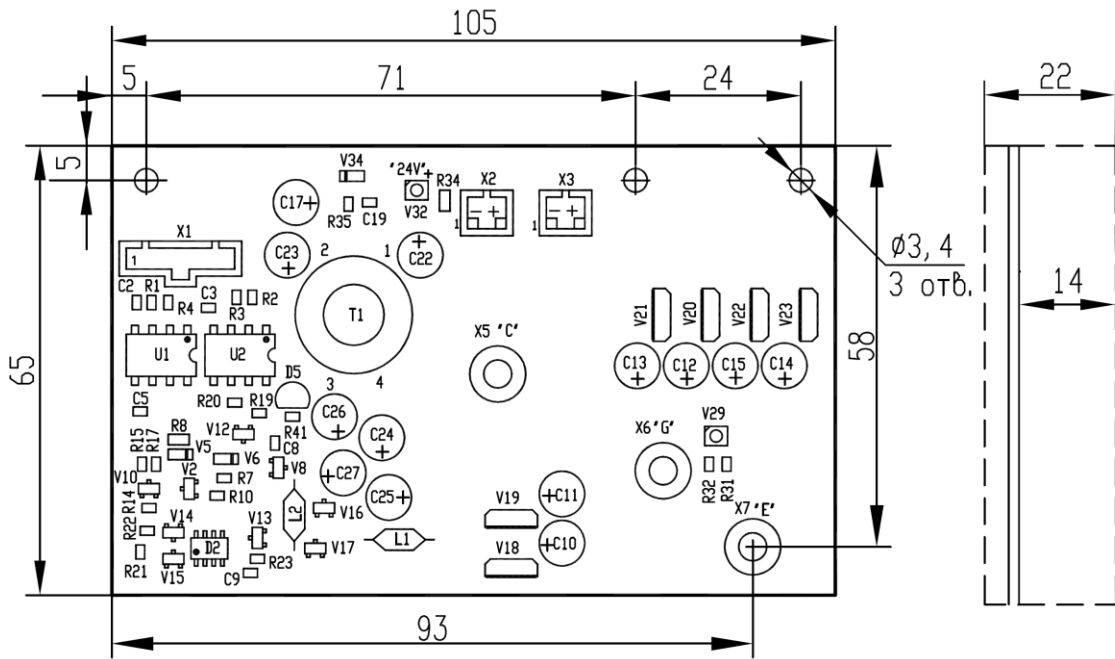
Габаритные и установочные размеры платы драйвера ДРИ11-20-17-20П1Н-1
